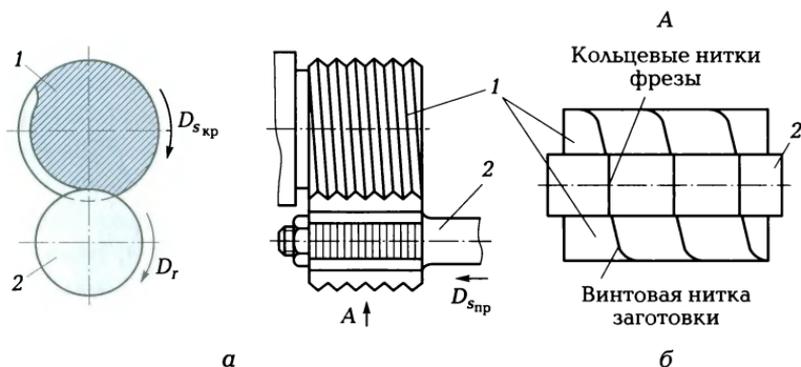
Резбофрезерование групповой (гребенчатой) фрезой: а — движения фрезы и заготовки; б — взаимное расположение ниток фрезы и заготовки: 1 — заготовка; 2 — фреза
